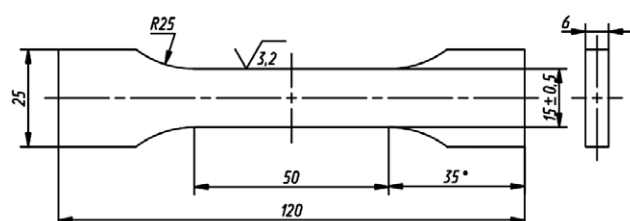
Размеры, мм, образца для испытания на растяжение: сварка напечатанного АМг5 и сплава 6082Т4.
